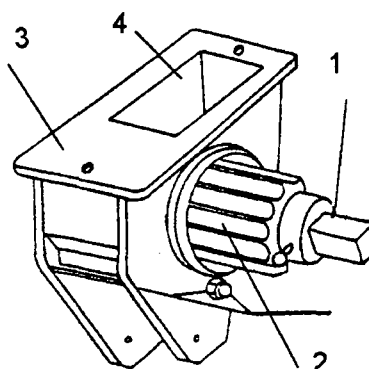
Dosador tipo rotor canelado - 1- eixo quadrado, 2 - rotor de cilindro canelado, 3 - caixa, 4 - posição do regulador de vazão - [8].
